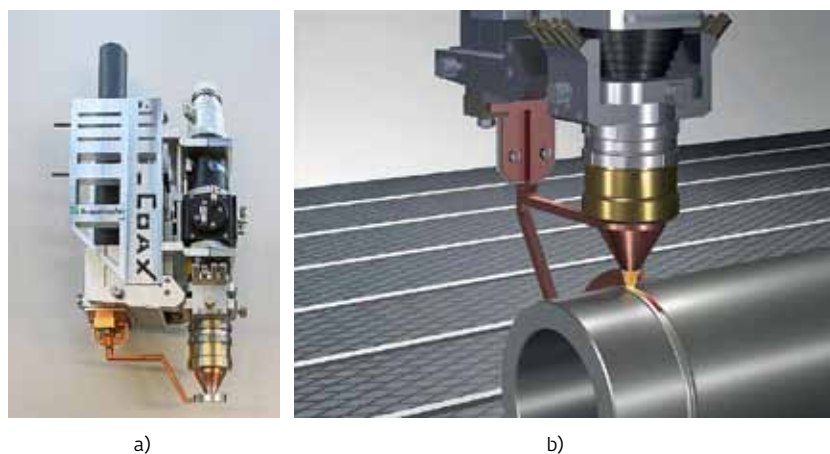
Лазерная головка для наплавки CoaxPowerLine: а) – общий вид; б) – процесс наплавки
